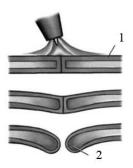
Несплавление кромок алюминиевых конструкций: 1 – оксидная пленка; 2 – чистый алюминий
